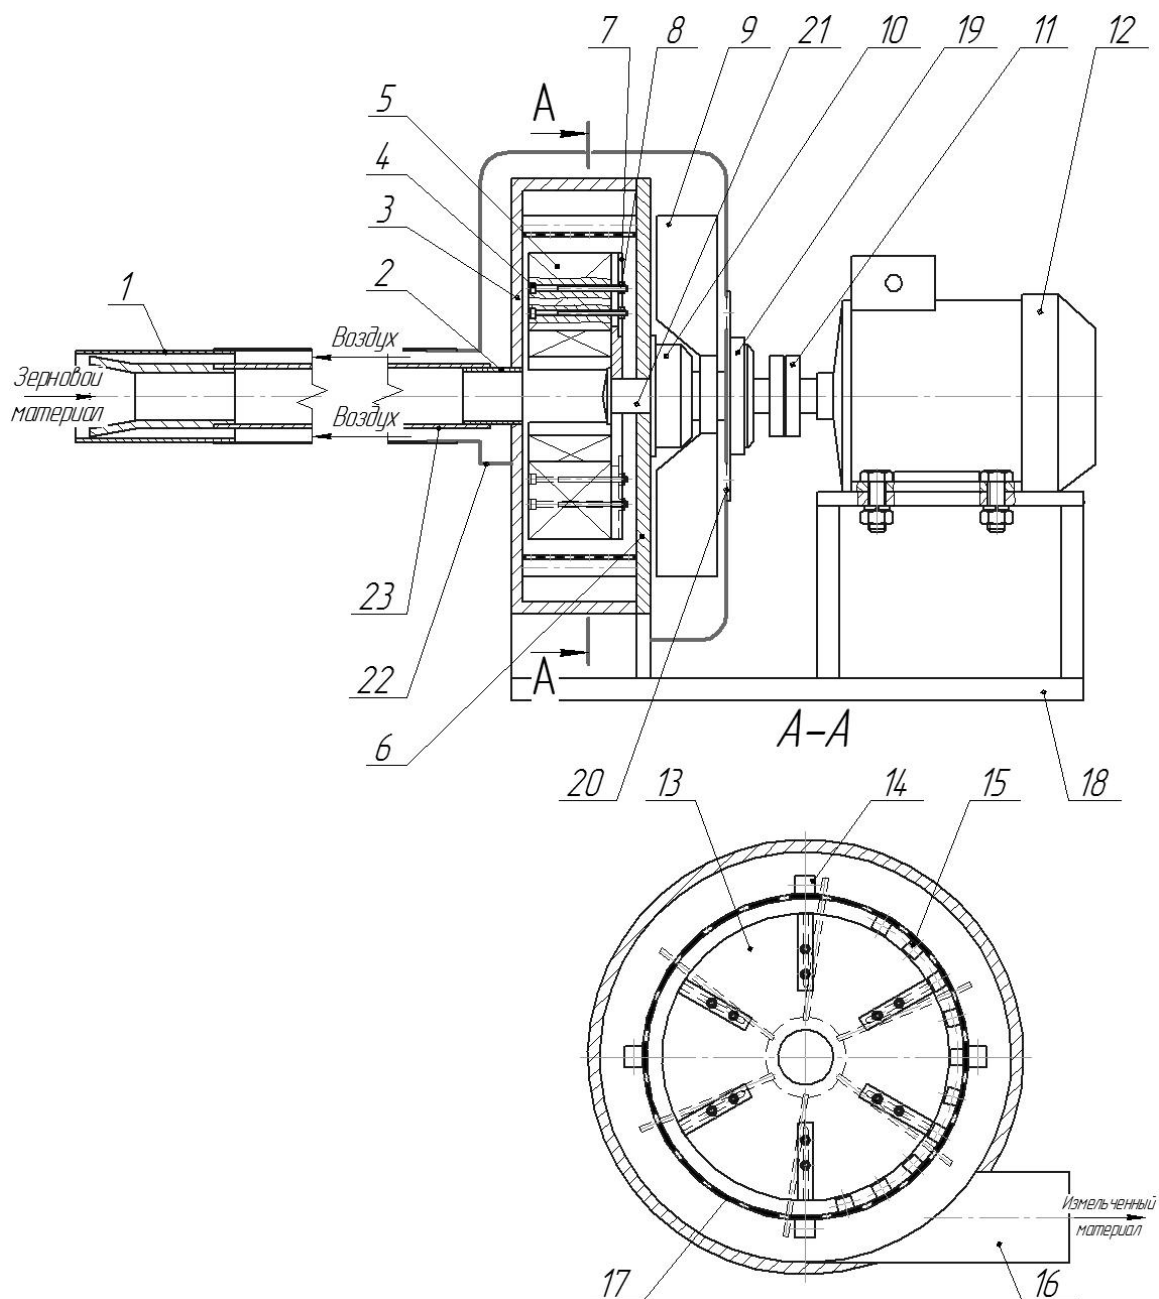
Схема перспективной конструкции центробежного измельчителя:
